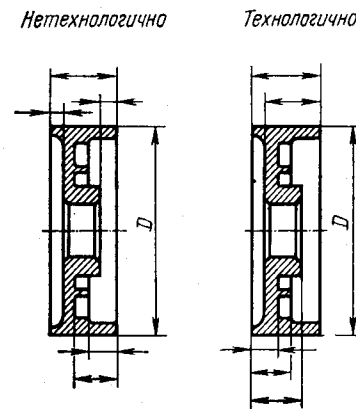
Простановка размеров на детали с наружными и внутренними поверхностями вращения.
